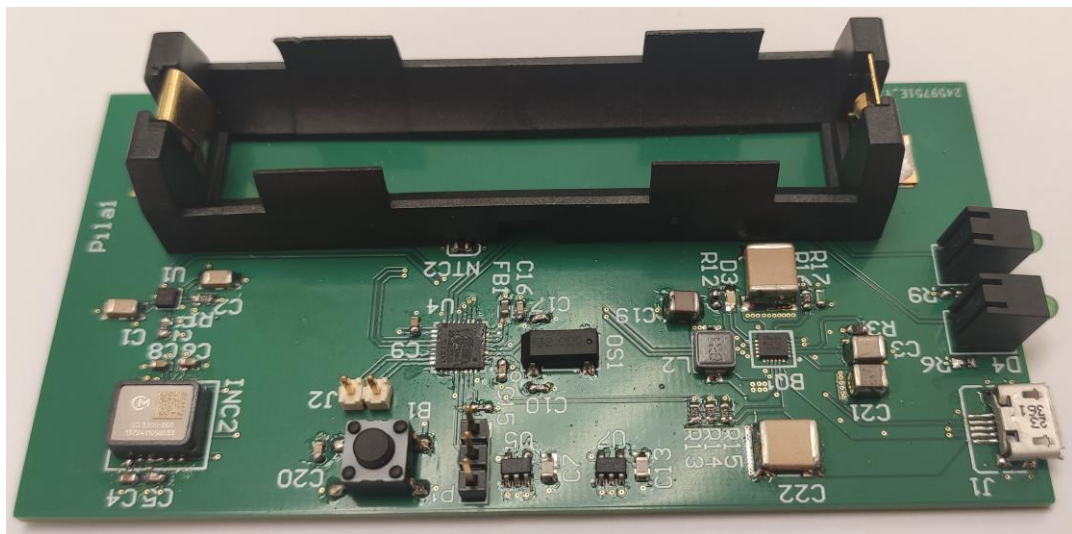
Imagen de la tarjeta fabricada y ensamblada.
